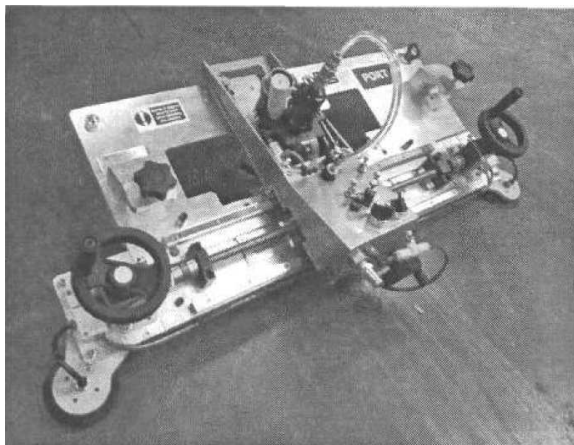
Общий вид ручного переносного инструмента для обрезки припуска
